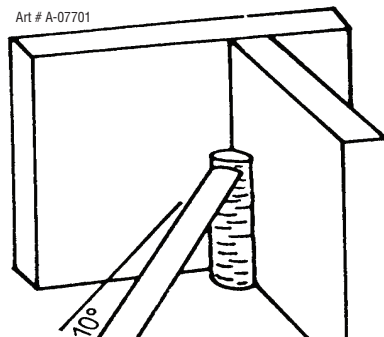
Soudure d'angle verticale à un seul passage
